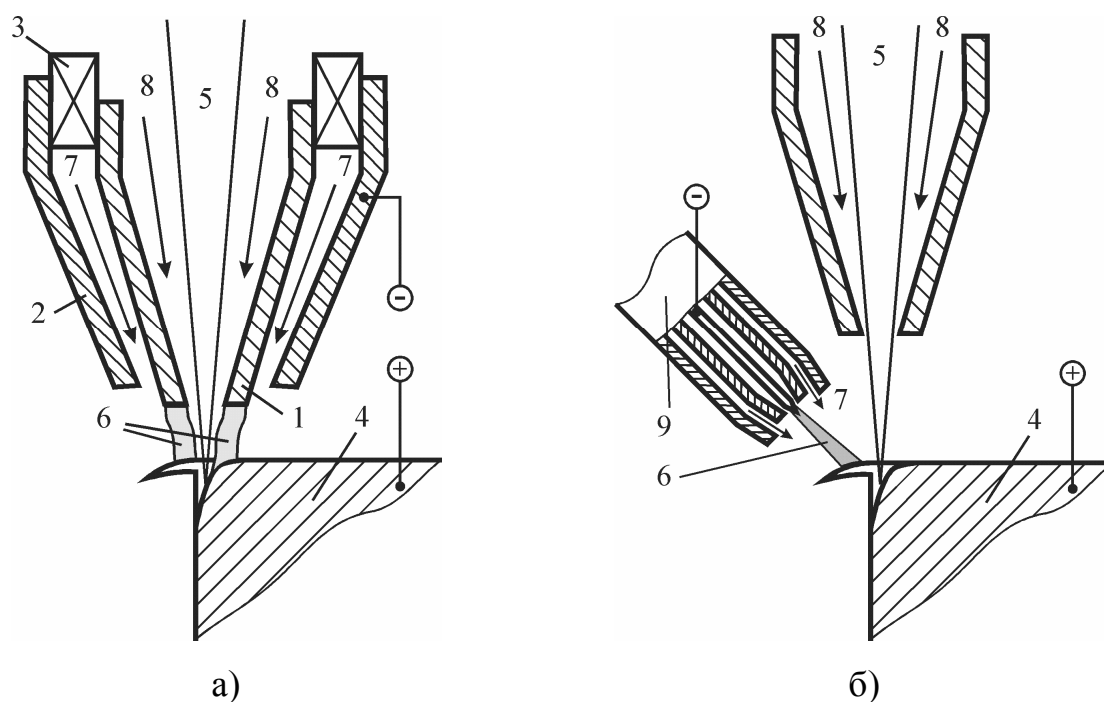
Схемы комбинированной лазерно-дуговой (а) и лазерно-плазменной (б) обработки: 1 – кольцевой катод; 2 – сопло; 3 – изолятор; 4 – обрабатываемая кромка; 5 – лазерный луч; 6 – дуга; 7, 8 – подача защитного газа; 9 – плазмотрон
